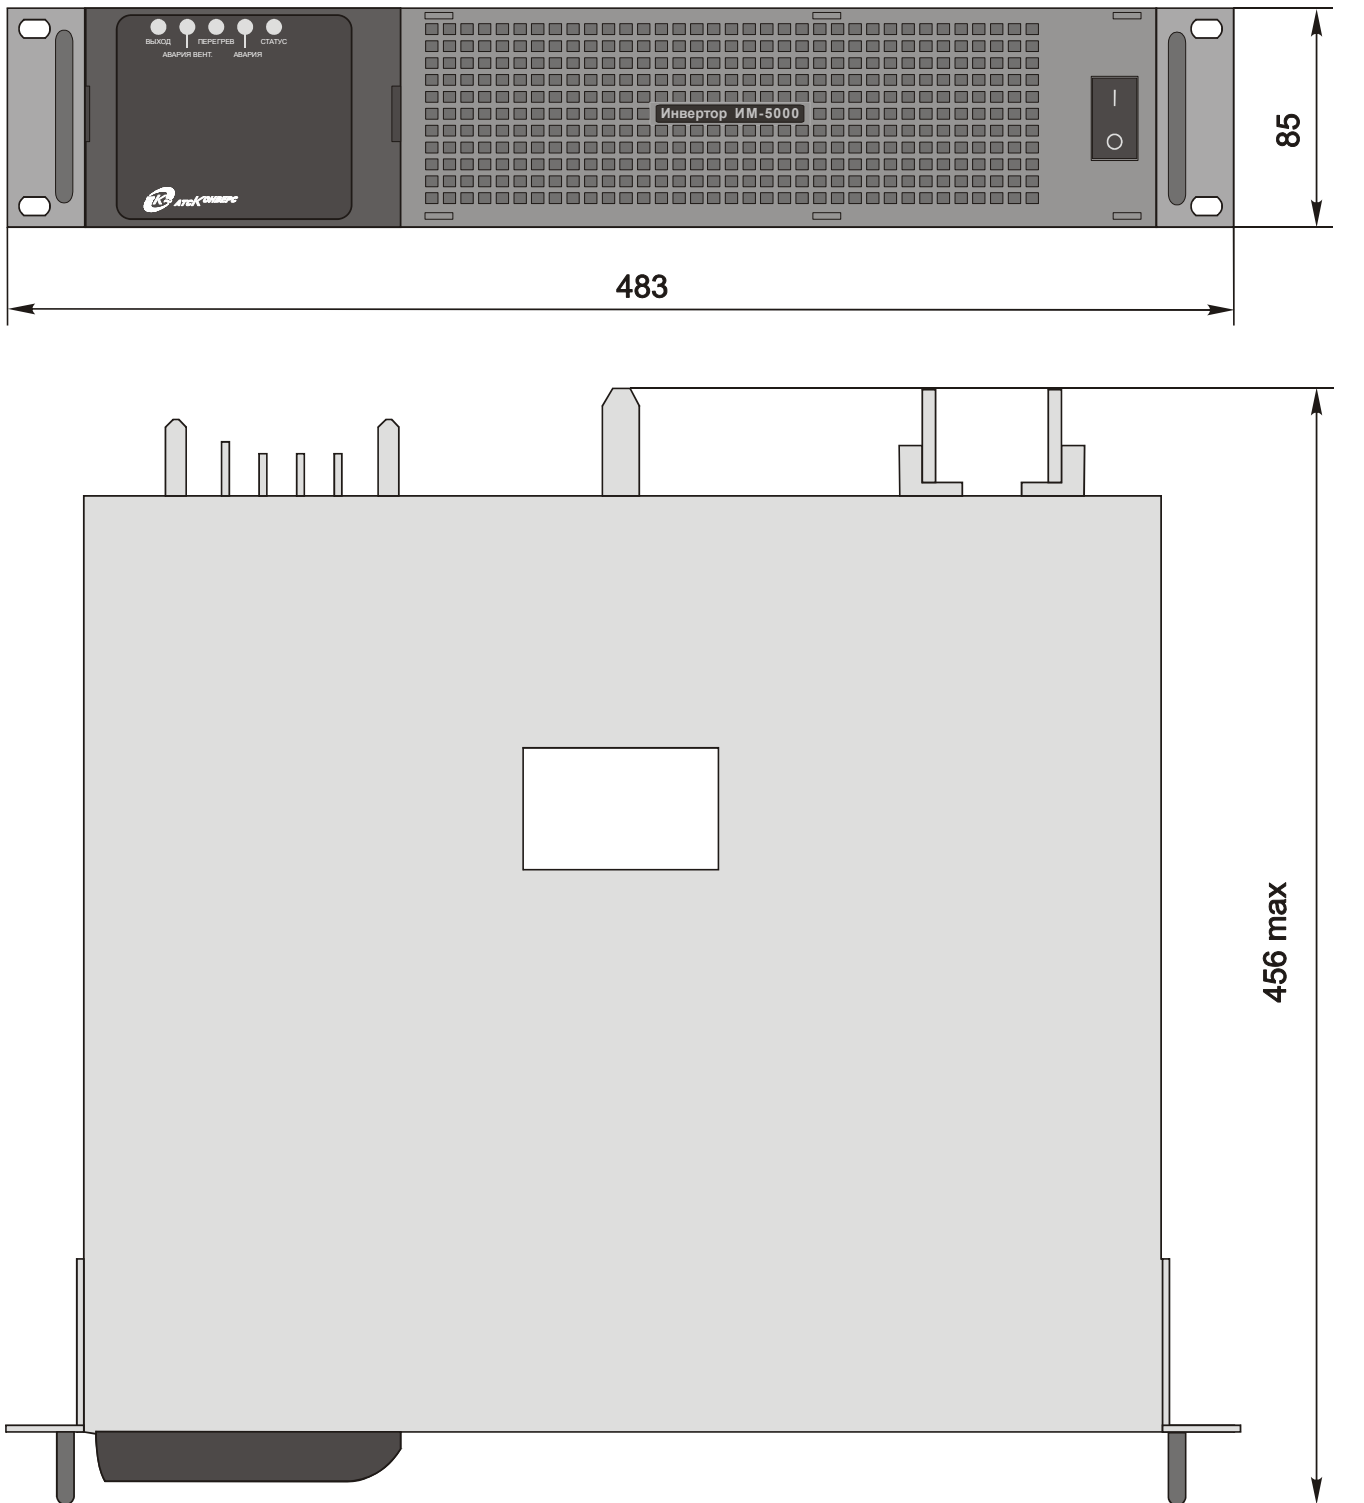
Внешний вид и габаритные размеры инвертора ИМ-5000
